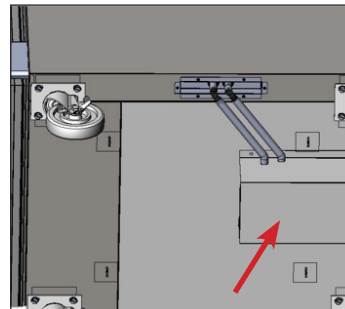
Soporte de la bandeja de drenaje calefaccionada colocado y mangueras instaladas.
